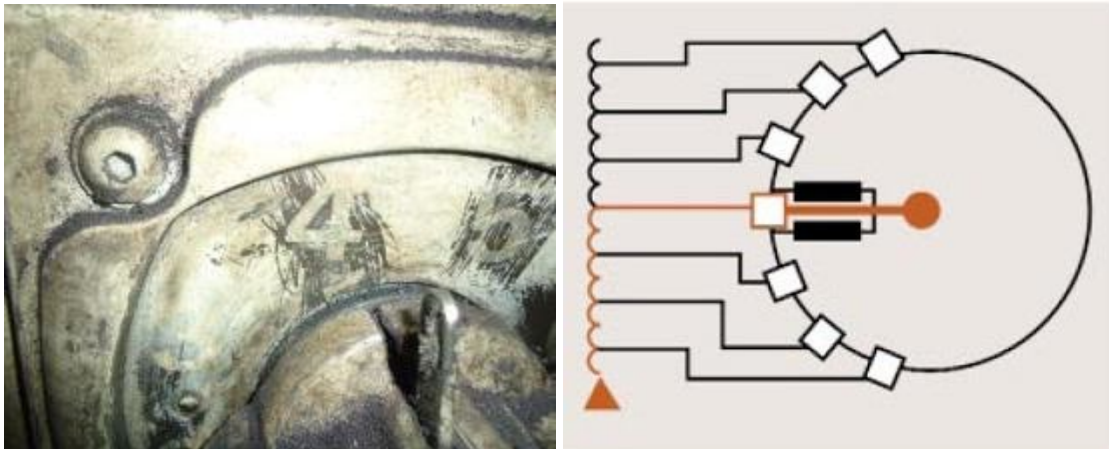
A la izquierda, selector de posición (*tap selector*) soldador Swift-Ohio 91AA del soldador usado en esta investigación, Fuente: Autor. Derecha, Principio eléctrico para un selector eléctrico tipo *on-load tap changer*, Fuente: <http://onloadtapchangersforp>
